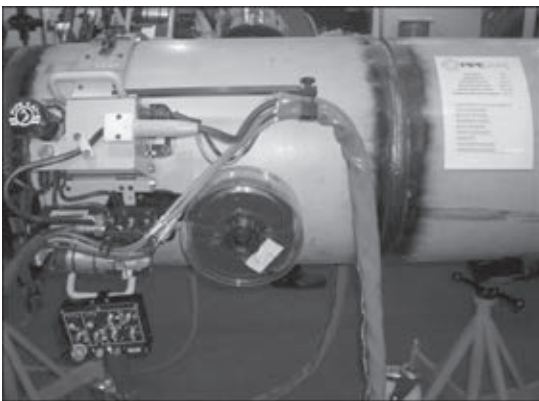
Система сварки неповоротных швов фирмы «GUL-LKO» (Канада)
